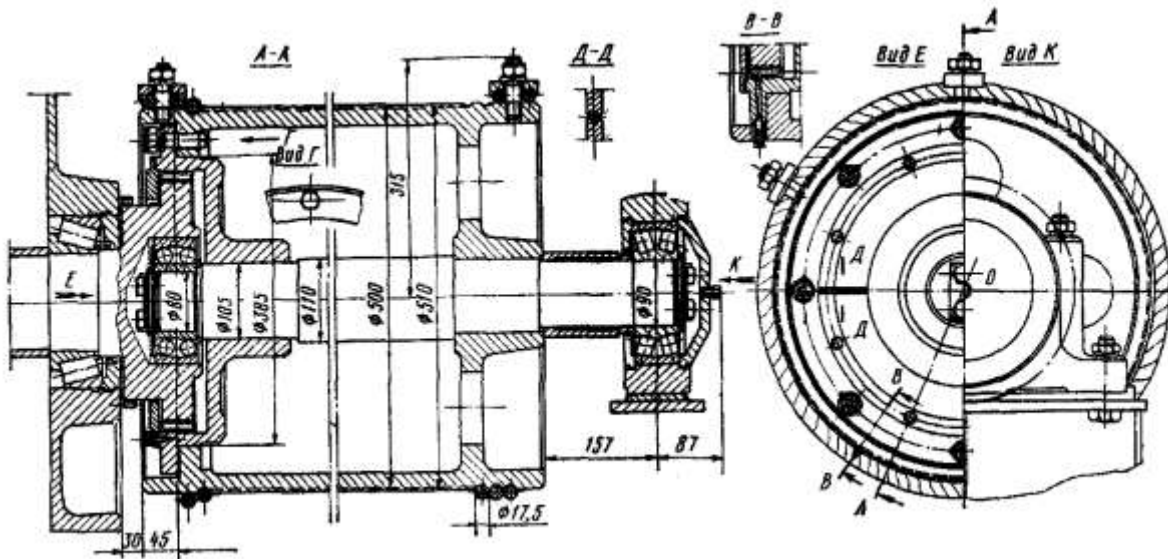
Типовая конструкция соединения барабана с валом редуктора при помощи зубчатой муфты
